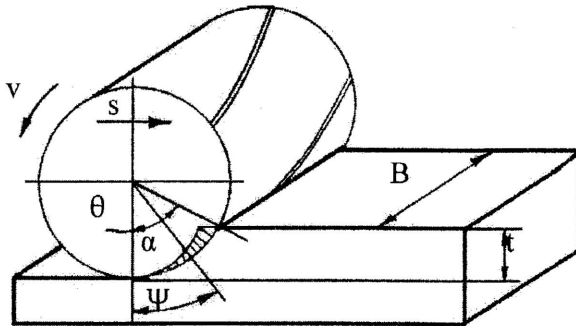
Кинематика среза припуска цилиндрической фрезой
